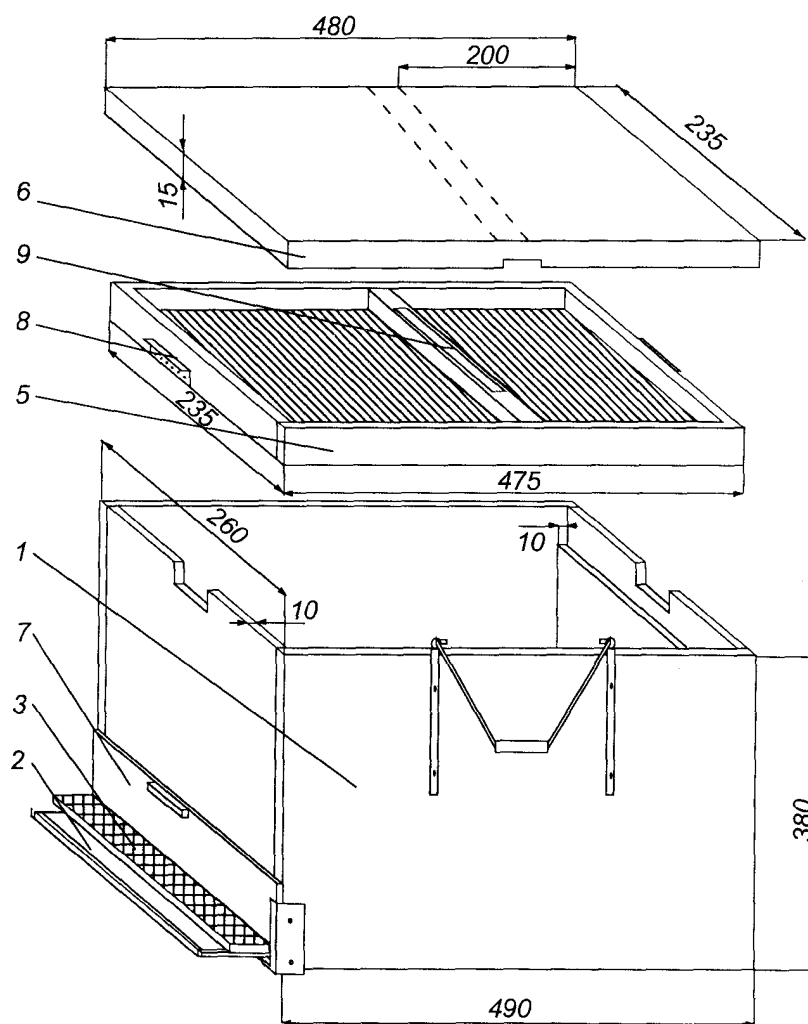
Конструкція переносного ящика-вулика [30, 26]
